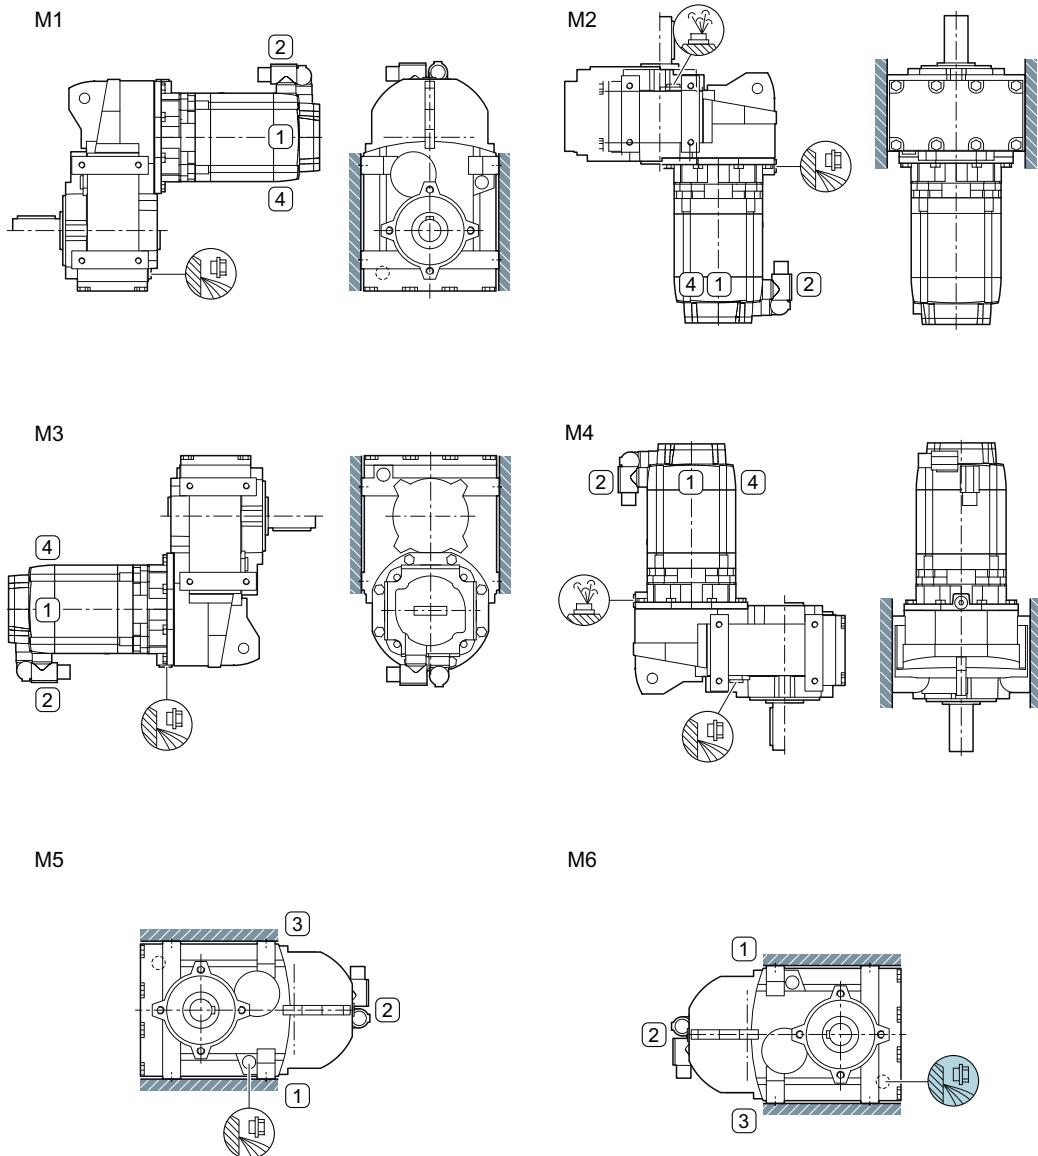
Einbaulagen für Servo-Flachgetriebemotoren FZ und FD, Fußausführung, Baugrößen 29, 2-stufig und 3-stufig
